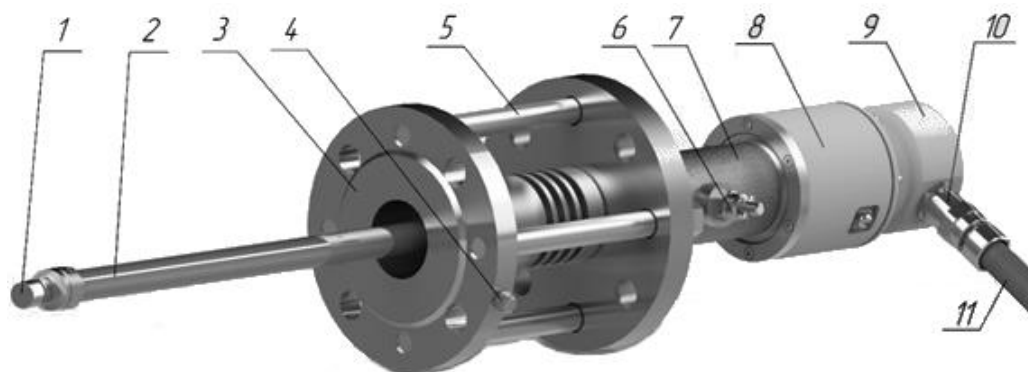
Приемопередатчик ФЛ ЛБ, без установочного приспособления
